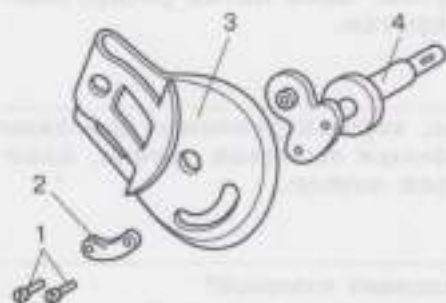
Детали вращающегося нитепритягивателя машины 97-А класса: 1 — винты; 2 — прокладка; 3 — нитепритягиватель; 4 — палец кривошипа
